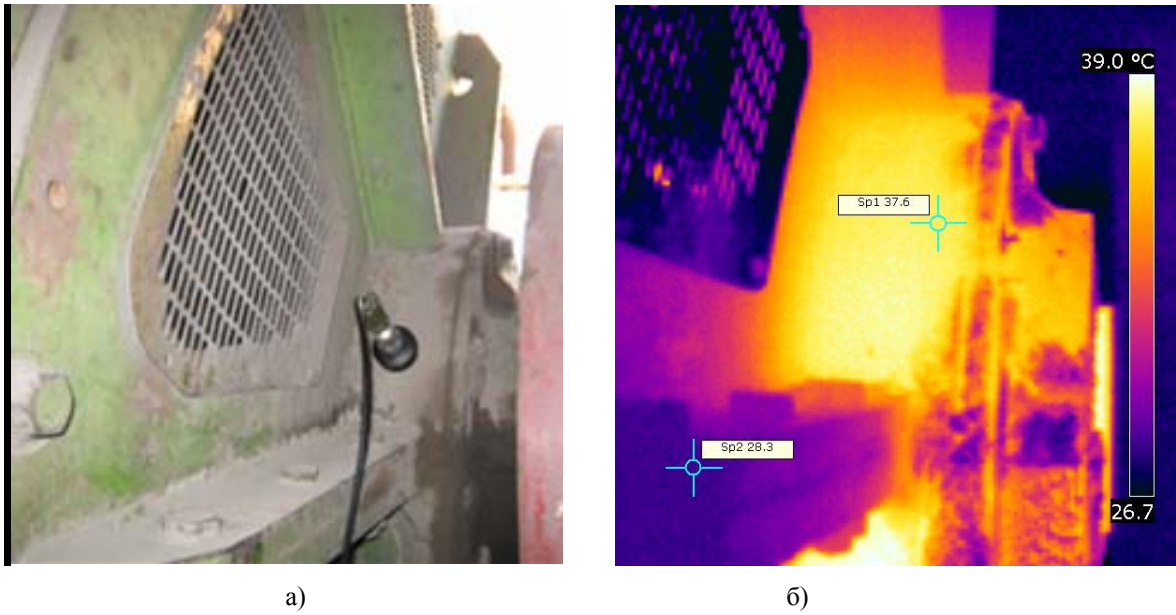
Фото (а) и инфракрасный снимок (б) подшипникового узла сетевого двигателя преобразовательного агрегата ЭШ – 10/70.
